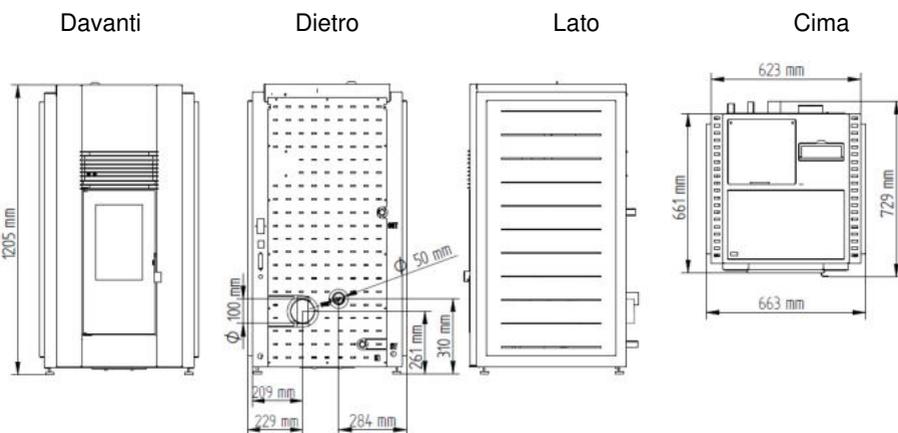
Dimensioni della stufa a pellet (versione acqua – Douro 23 kW)
